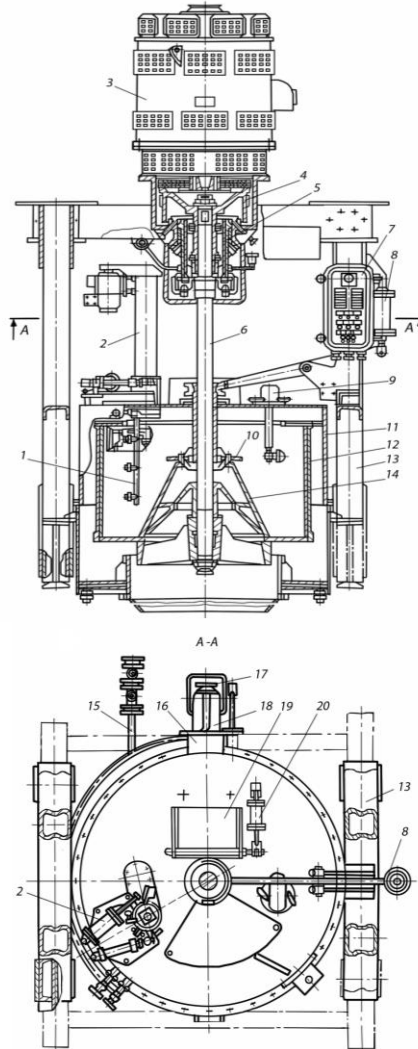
Автоматична центрифуга ФПН-1251Л-02: 1 – промивний пристрій; 2 – механізм зрізу; 3 – електродвигун; 4 – механічне
